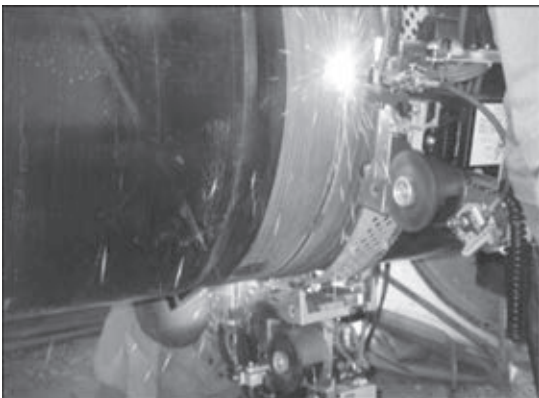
Система сварки неповоротных швов фирмы «PWT» (Италия)
